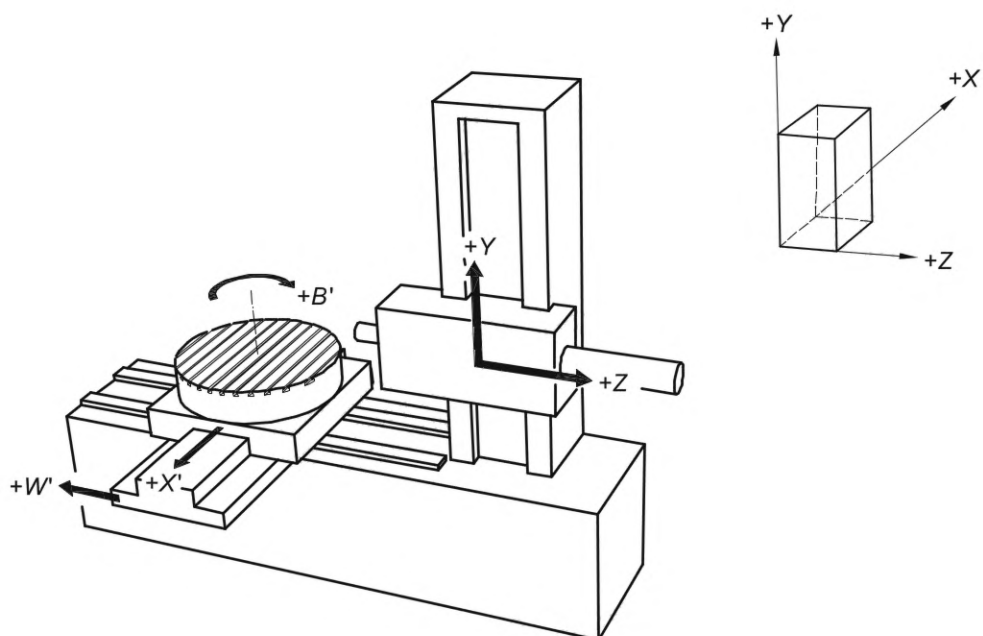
Расточно-фрезерный горизонтальный станок
